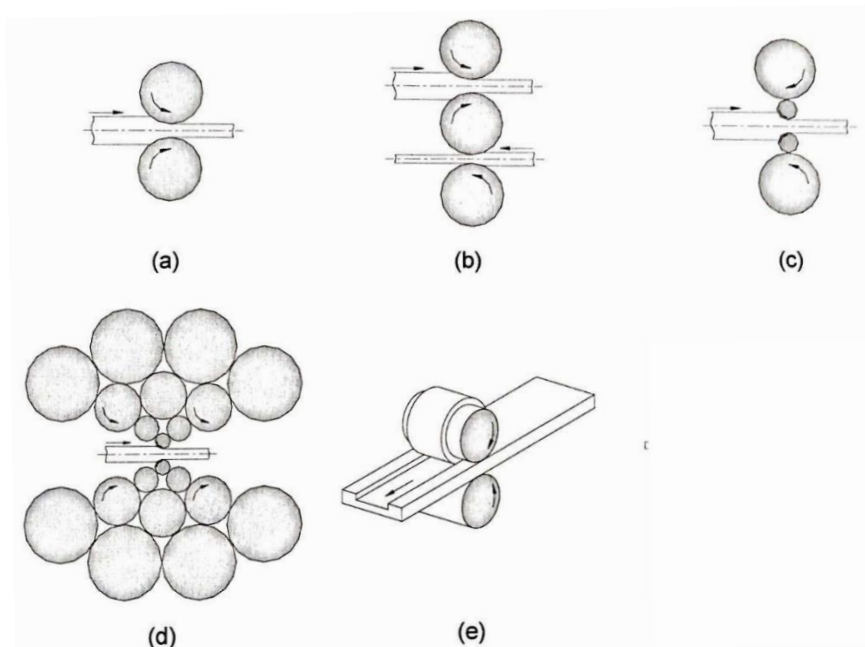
Representação esquemática dos tipos de laminadores industriais; a) laminador duo; b) laminador trio; c) laminador de quatro rolos; d) laminador Sendzimir; e) laminador de produtos não-planos [2].
